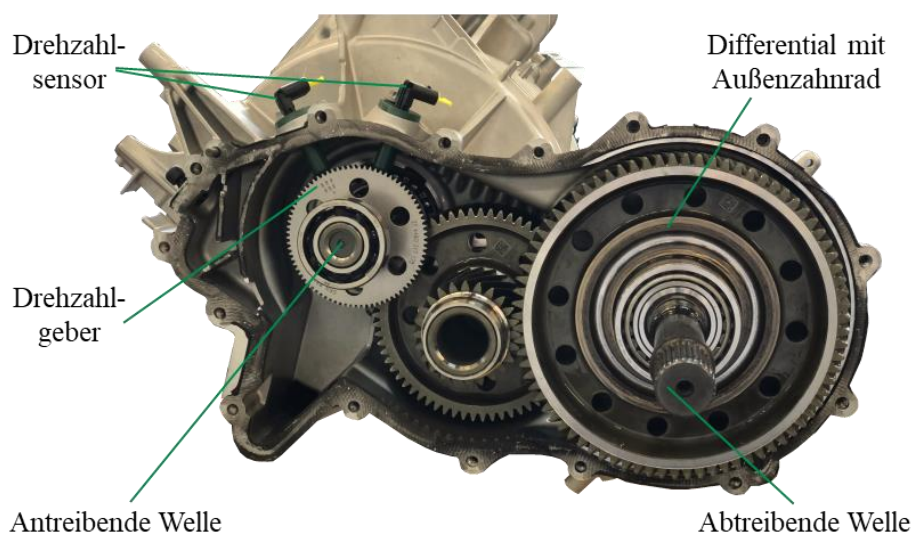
Geöffnetes Getriebe des EAA mit Sicht auf zwei schrägverzahnte Stirnradpaare
